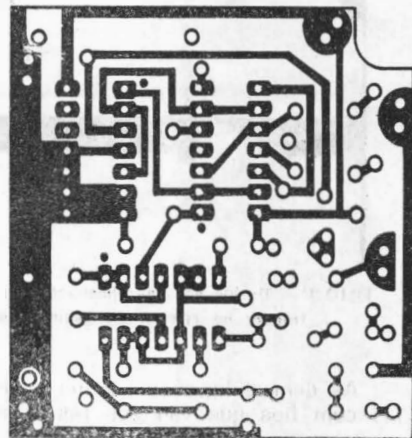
Desenho da face cobreada da plaqueta de circuito impresso para o rastreador.
